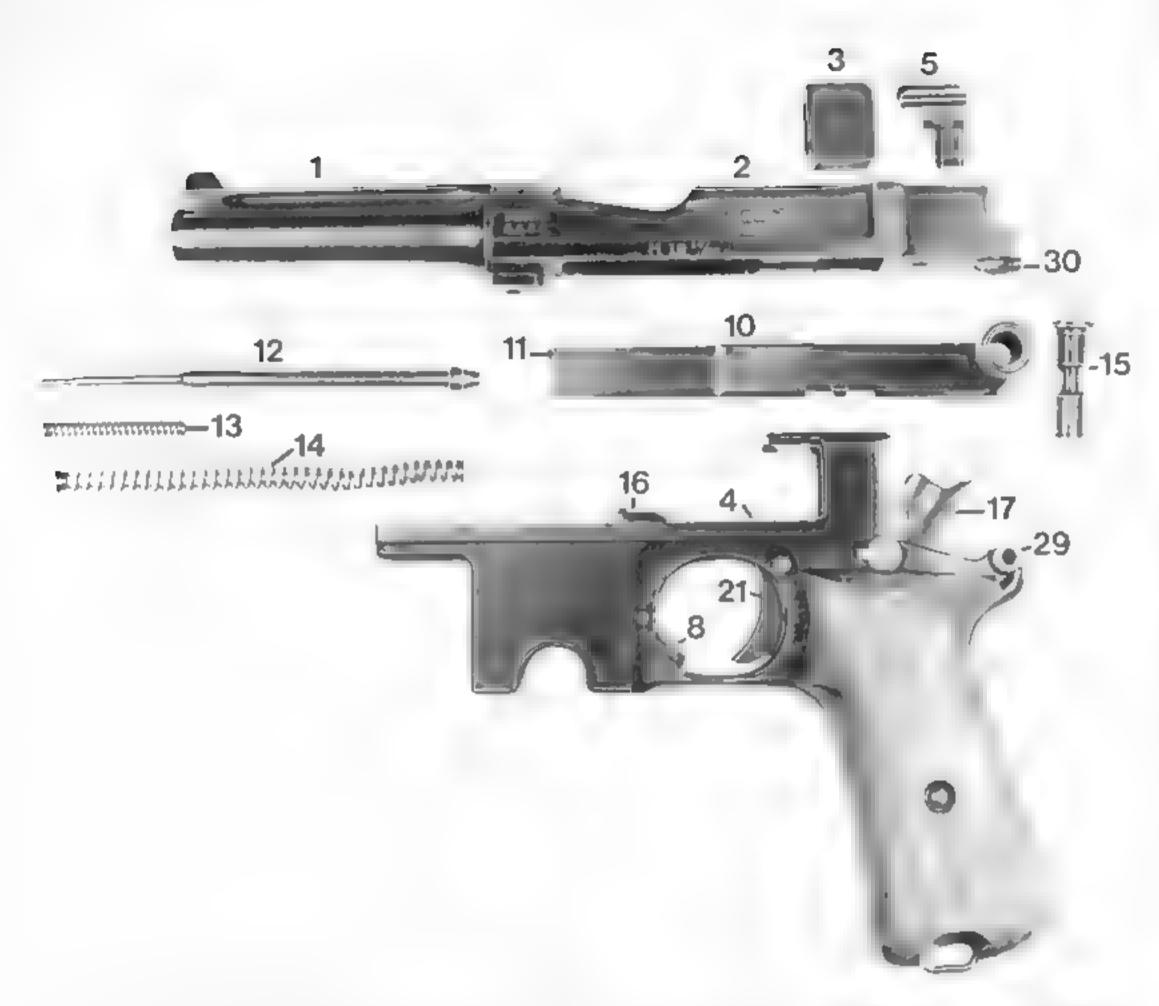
Pistole zerlegt: 1 = Lauf, 2 = Schlitten, 3 = Verriegelungsstück, 4 = Griffstück, 5 = Kimmenstück, 8 = Magazinhalter, 10 = Verschlußstück, 11 = Auszieher, 12 = Schlagbolzen, 13 = Schlagbolzenfeder, 14 = Schließfeder, 15 = Haltebolzen, 16 = Auswerfer, 17 = Hammer, 21 = Abzug, 29 = Sicherungshebel, 30 = Nocken
